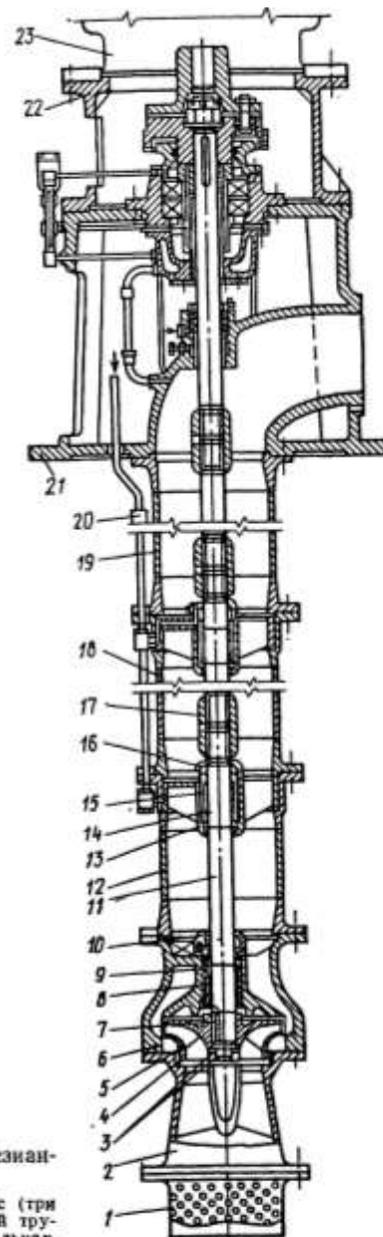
Конструкция одноколесного насоса 24А-18Х1:
